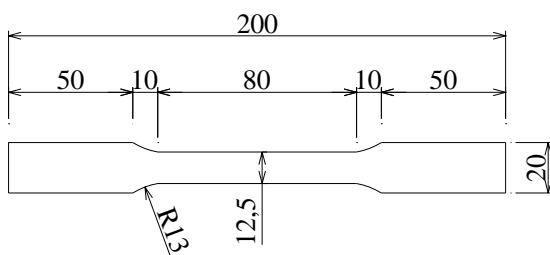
Dimensões dos corpos-de-prova conforme ASTM A370:2007 (dimensões em mm)
